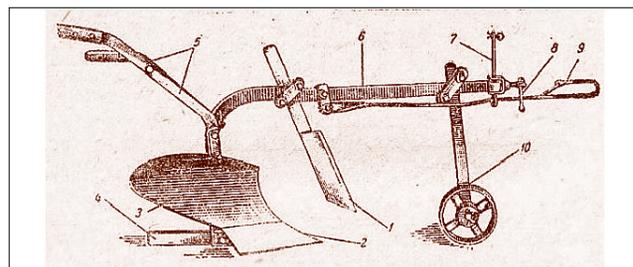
Висячий плуг ПВ-23: 1 – черенковый нож; 2 – лемех; 3 – отвал; 4 – полевая доска; 5 – ручка; 6 – грядиль; 7 – регулятор глубины вспашки; 8 – регулятор ширины захвата; 9 – упряжной крюк; 10 – колесо с поддерживающей стойкой
